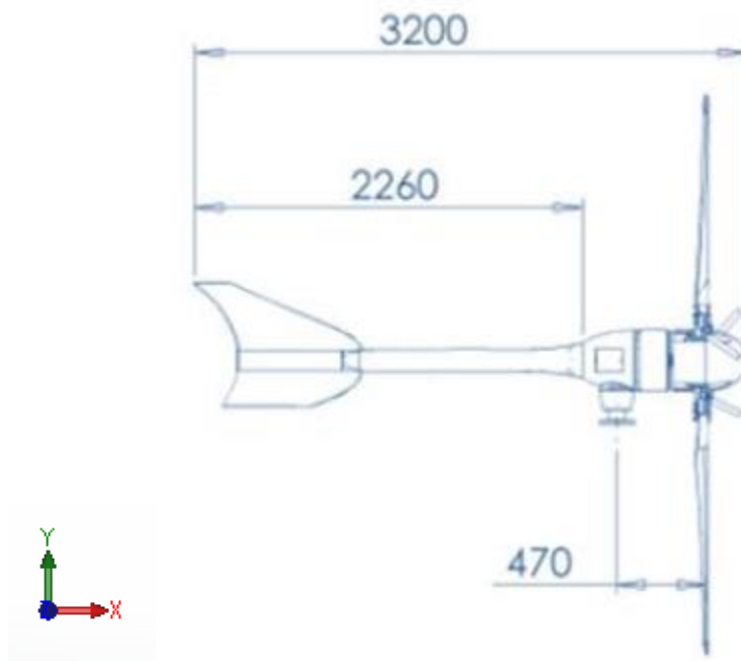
Croquis simplificado aerogenerador de perfil. FUENTE: WINDSPOT
